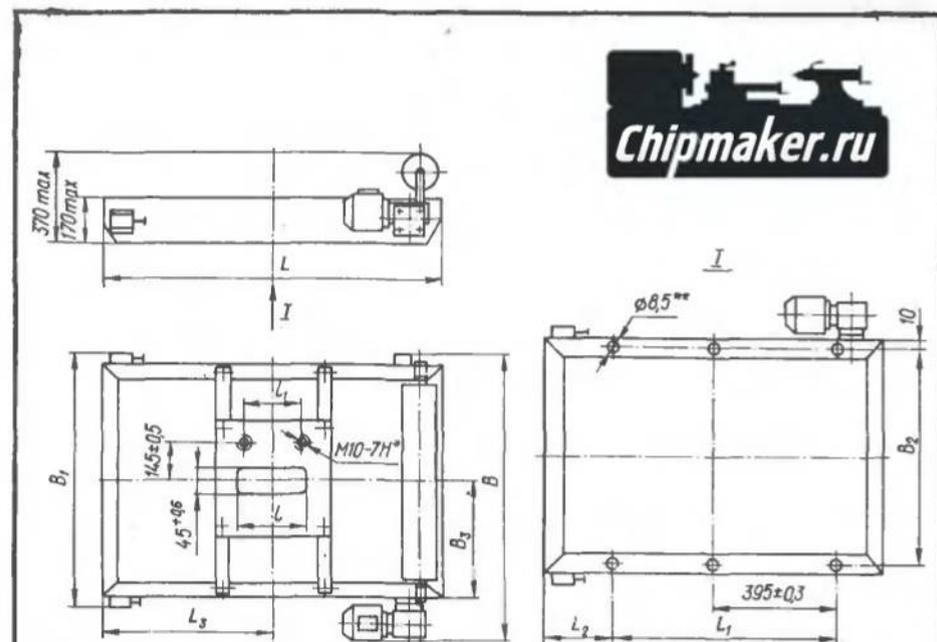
Габаритные и присоединительные размеры фильтров-транспортёров Х44-3:
